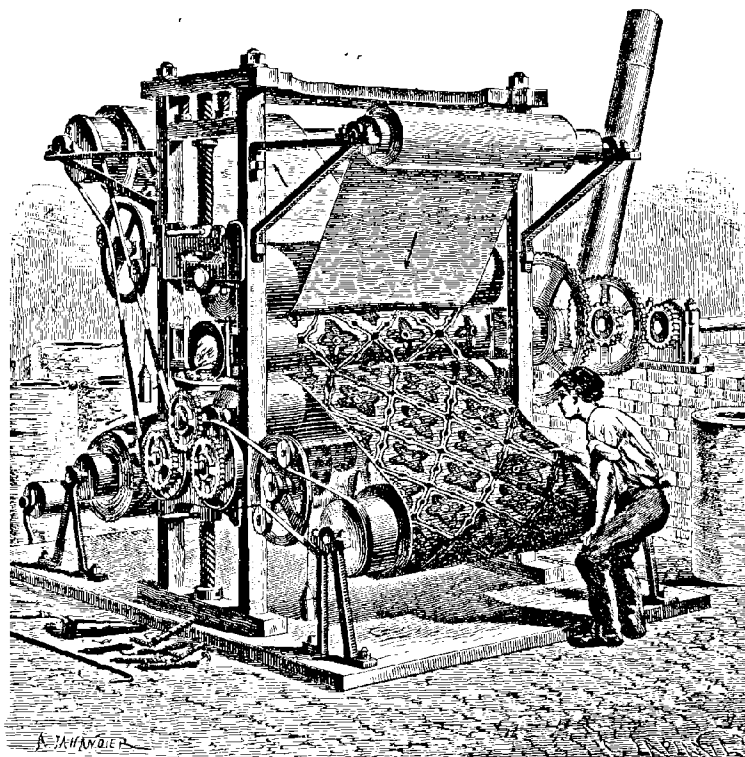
Machines à gaufrer le velours d'Utrecht.
